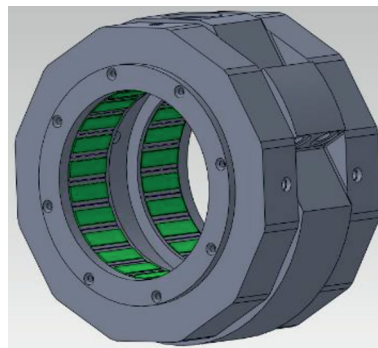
Вкладыш подшипника (вариант 2) со стержнями из твердого сплава
